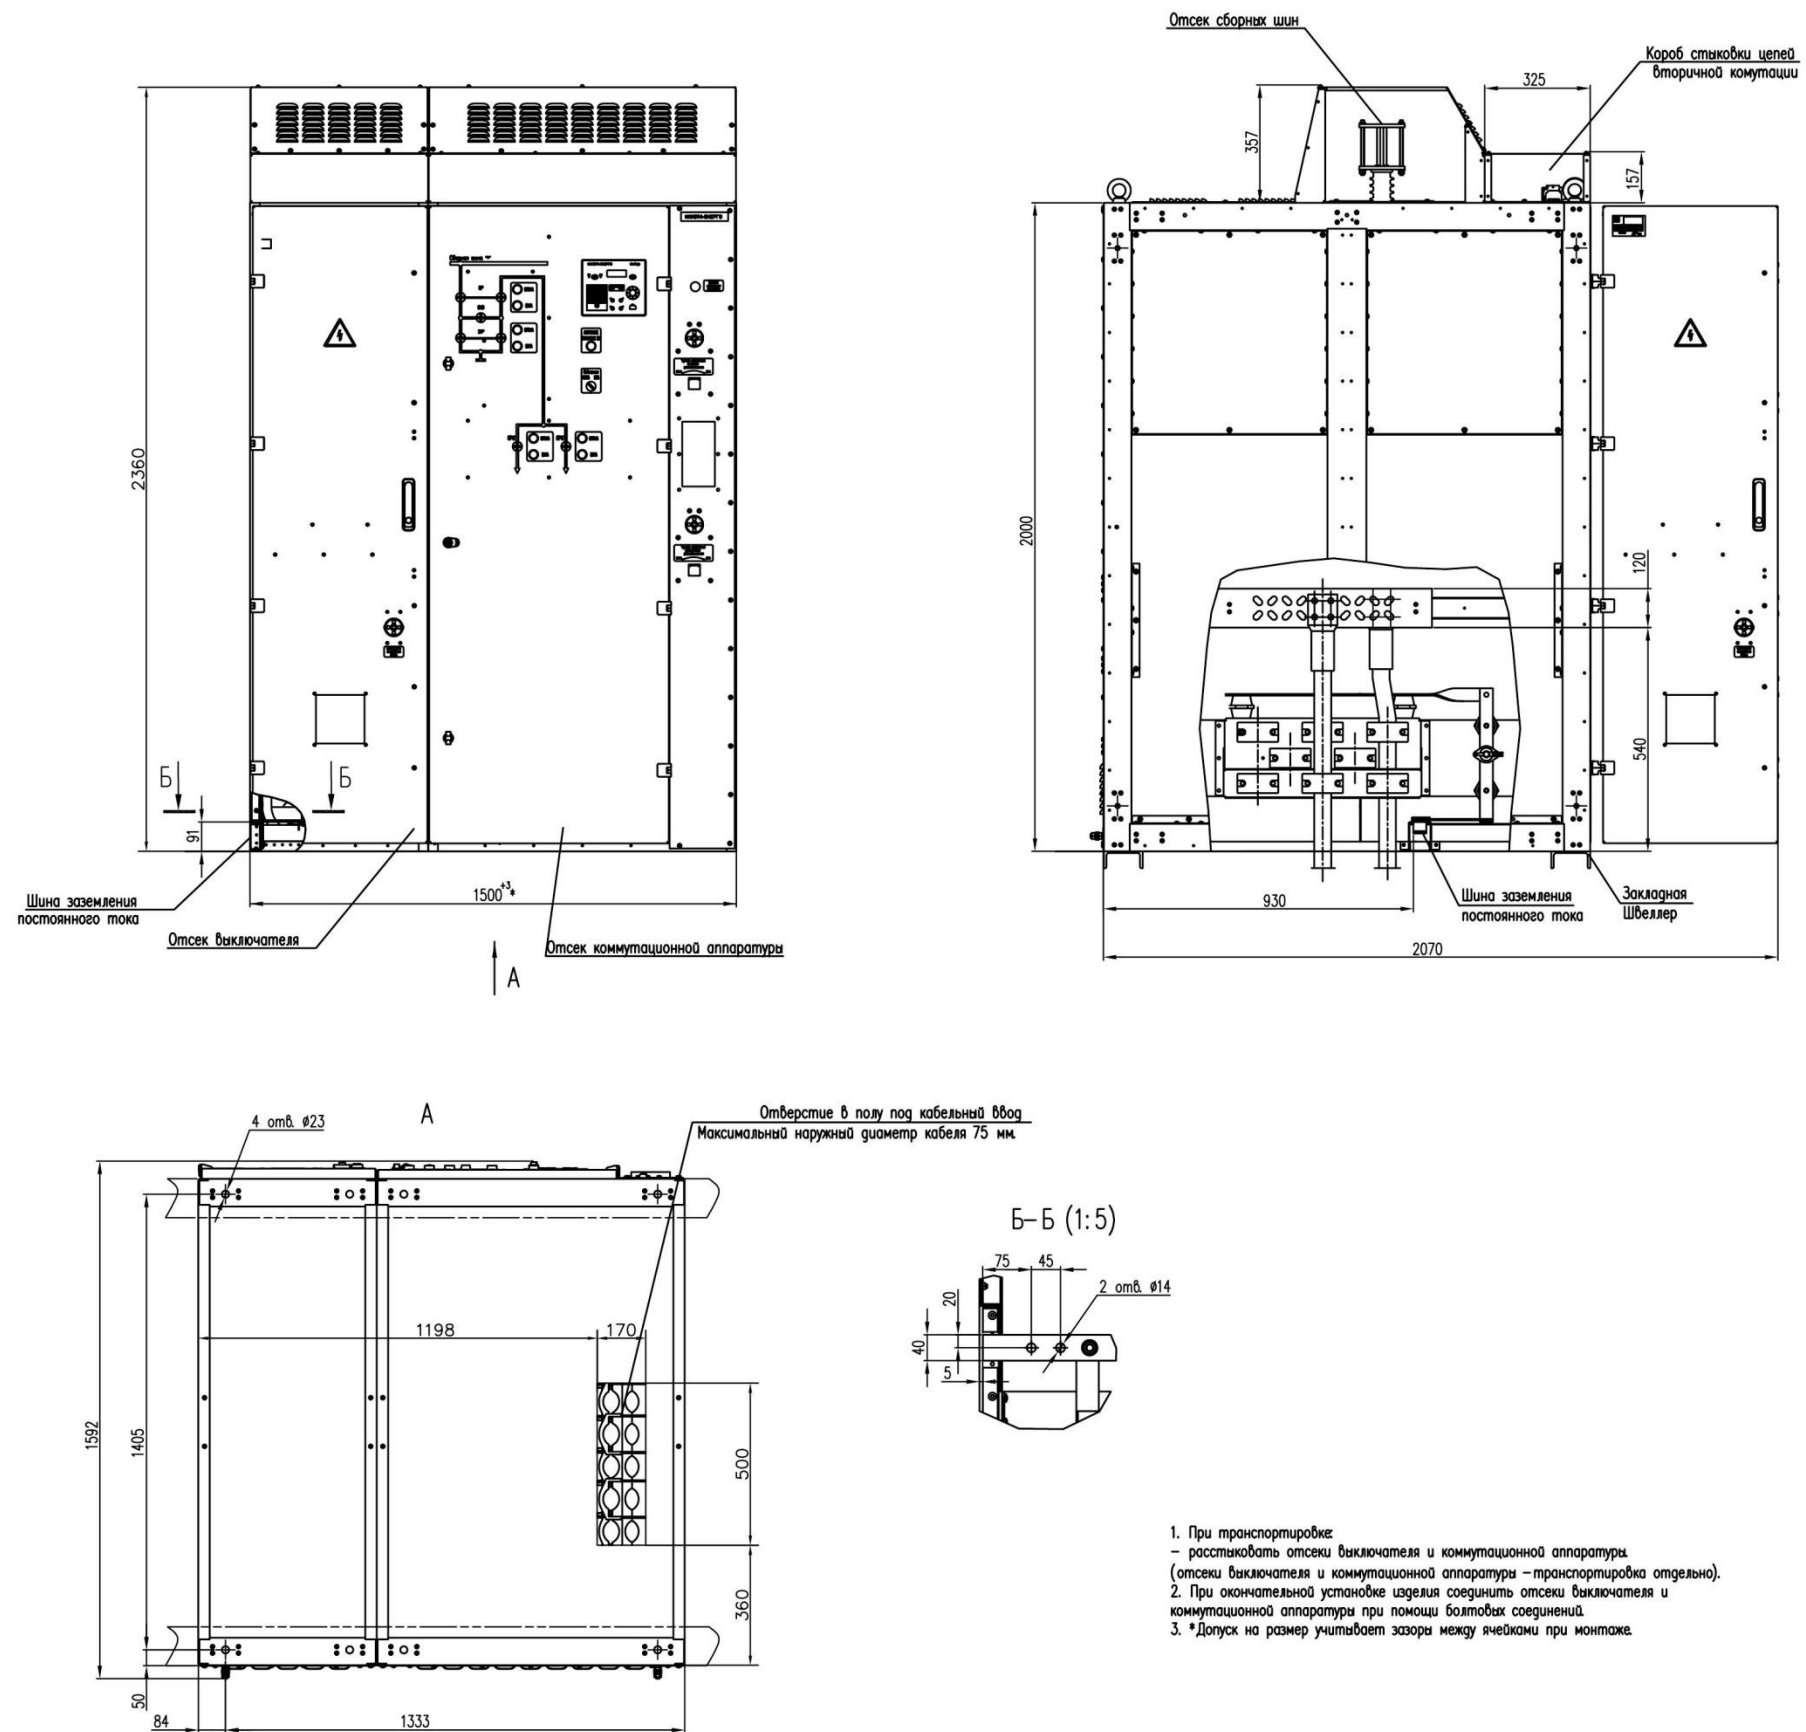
Ячейка резервного выключателя 1С-825-РВ-УХЛ4 номер схемы 03
